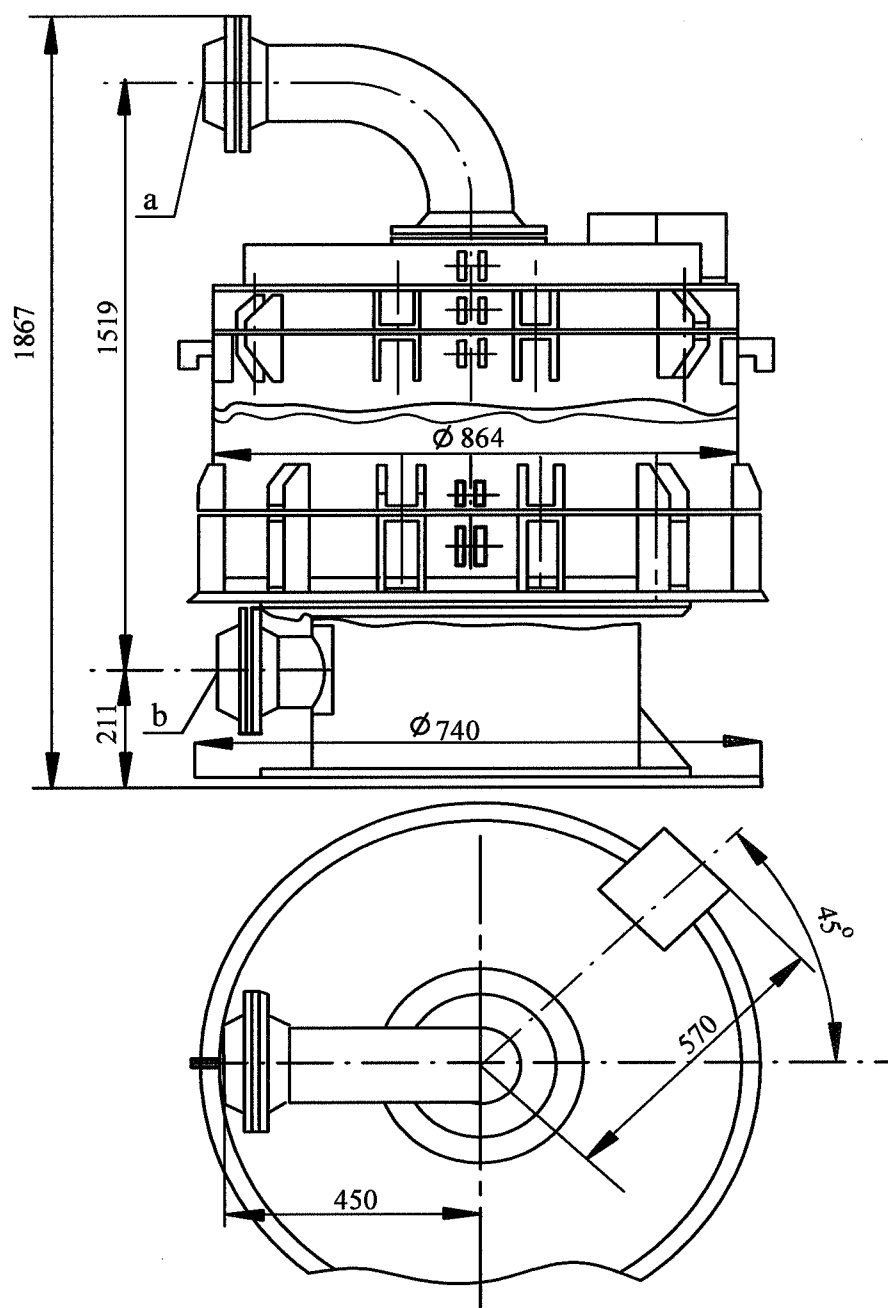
Габаритный чертеж аппарата контактного с электронагревателем
